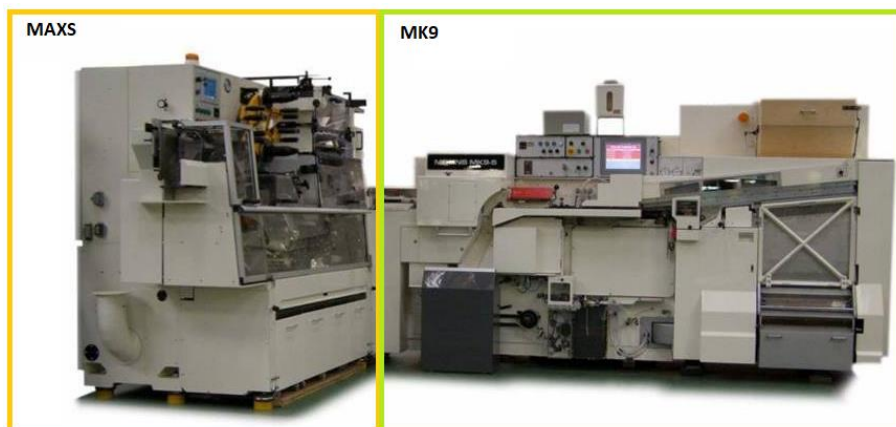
Máquina Elaboradora de Tabacos MK9 en conjunto con la Ensambladora de Filtros MAXS [7].
